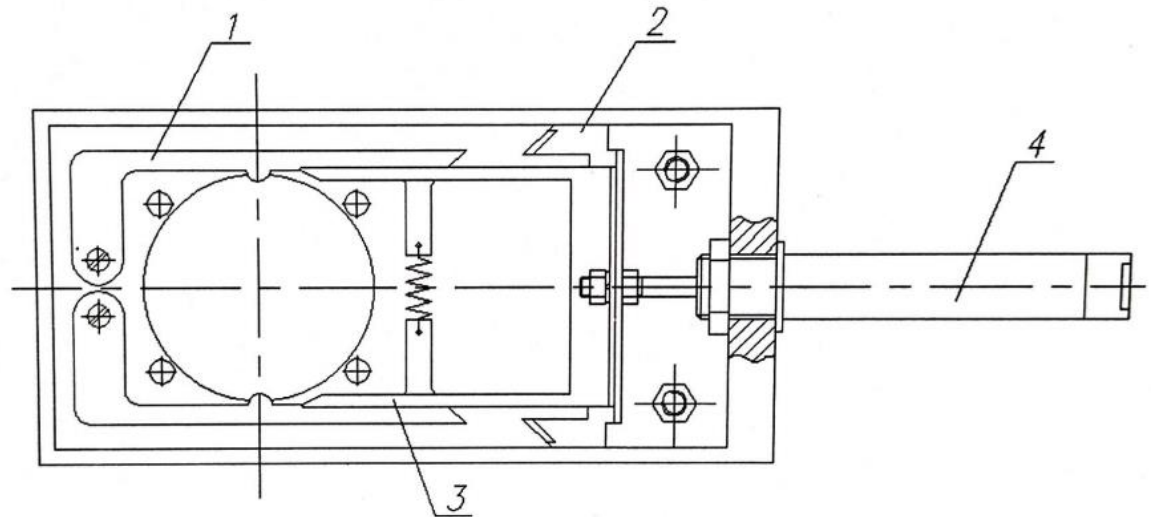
Ескіз механізму виділення стаканчиків (вид зверху): 1-фіксатор; 2-вилка; 3-захват; 4-пневмоциліндр.
